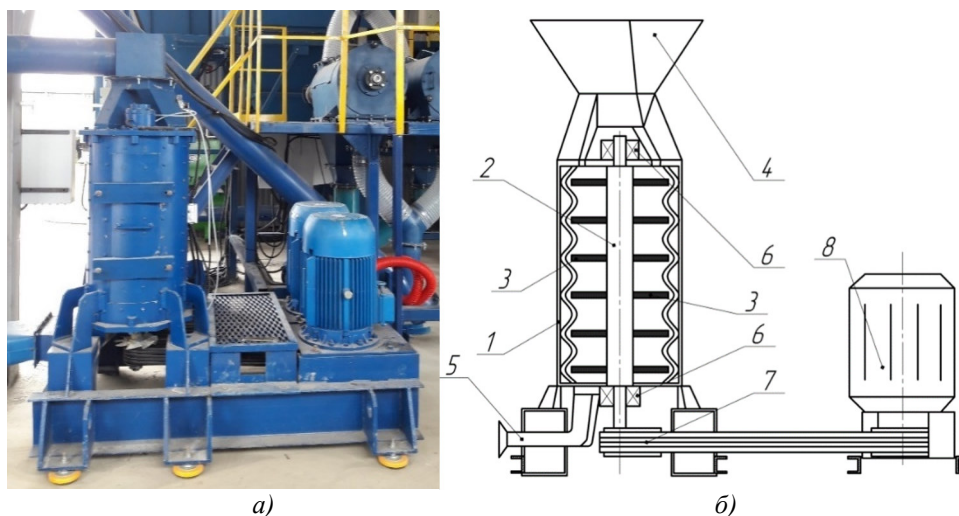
Роторно-вихревая мельница: а – вид на действующий агрегат; б – конструктивная схема: 1 – цилиндрический корпус со съемной футеровкой волнистого типа; 2 – корпус ротора; 3 – била; 4 – загрузочное отверстие; 5 – разгрузочное отверстие; 6 – подшипниковые опоры; 7 – редуктор, 8 – электродвигатель
